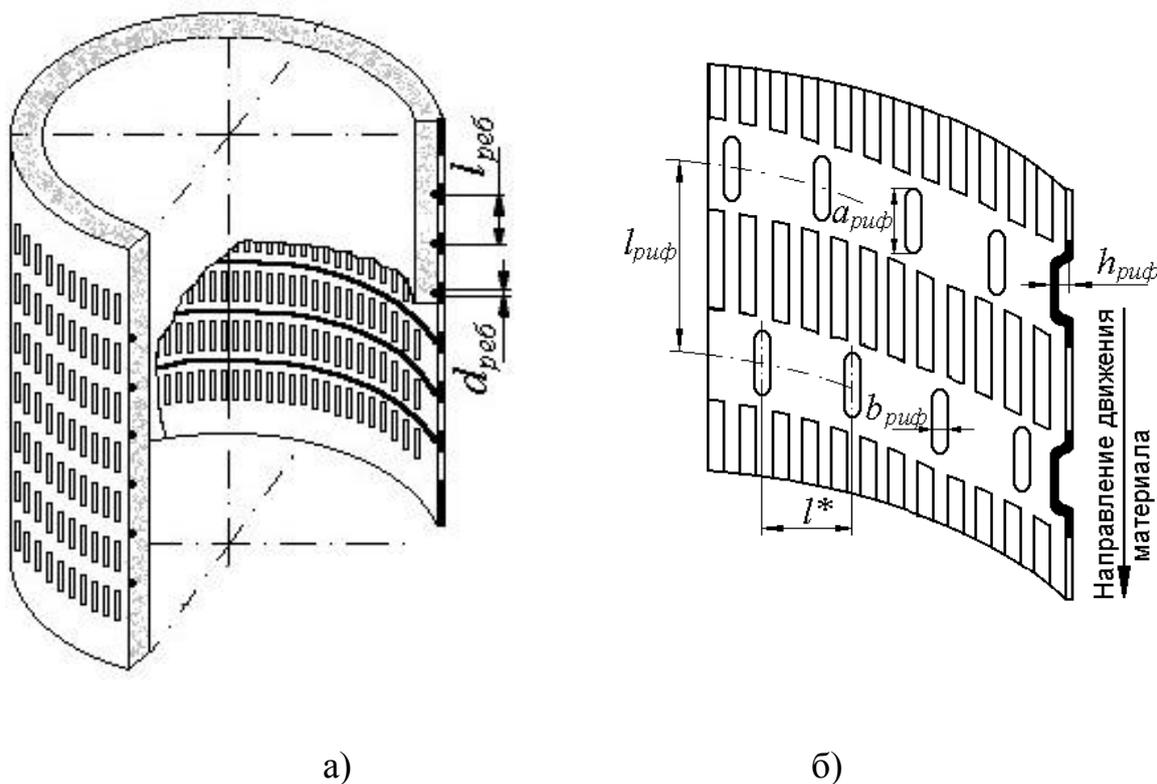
Конструктивные схемы цилиндрических решет с разрыхлителями:
